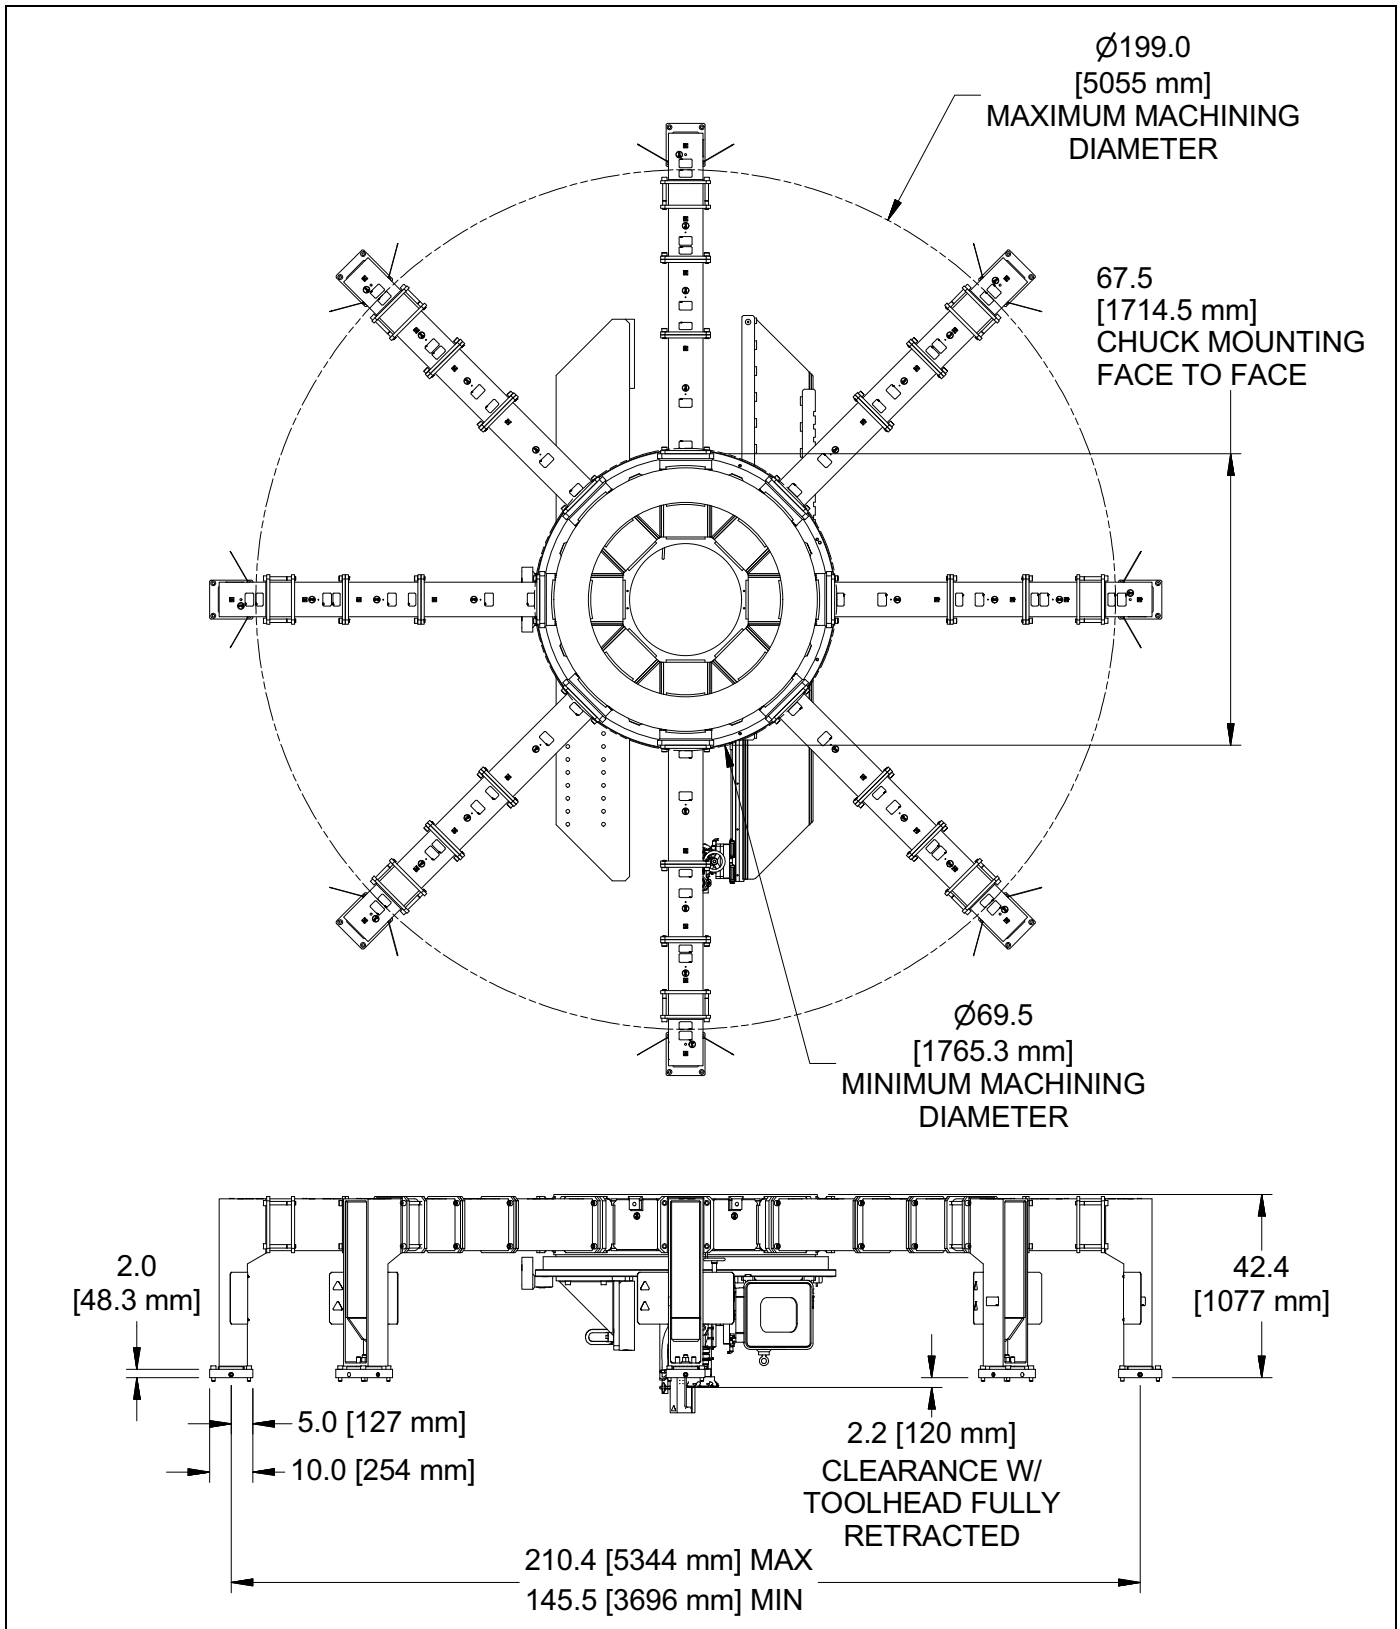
DIMENSIONS DE LA MACHINE À MONTAGE SUR DE
